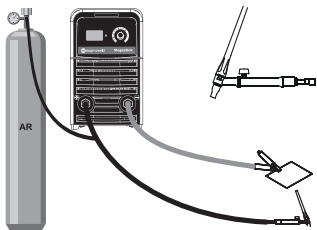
Подсоединения для TIG-сварки
